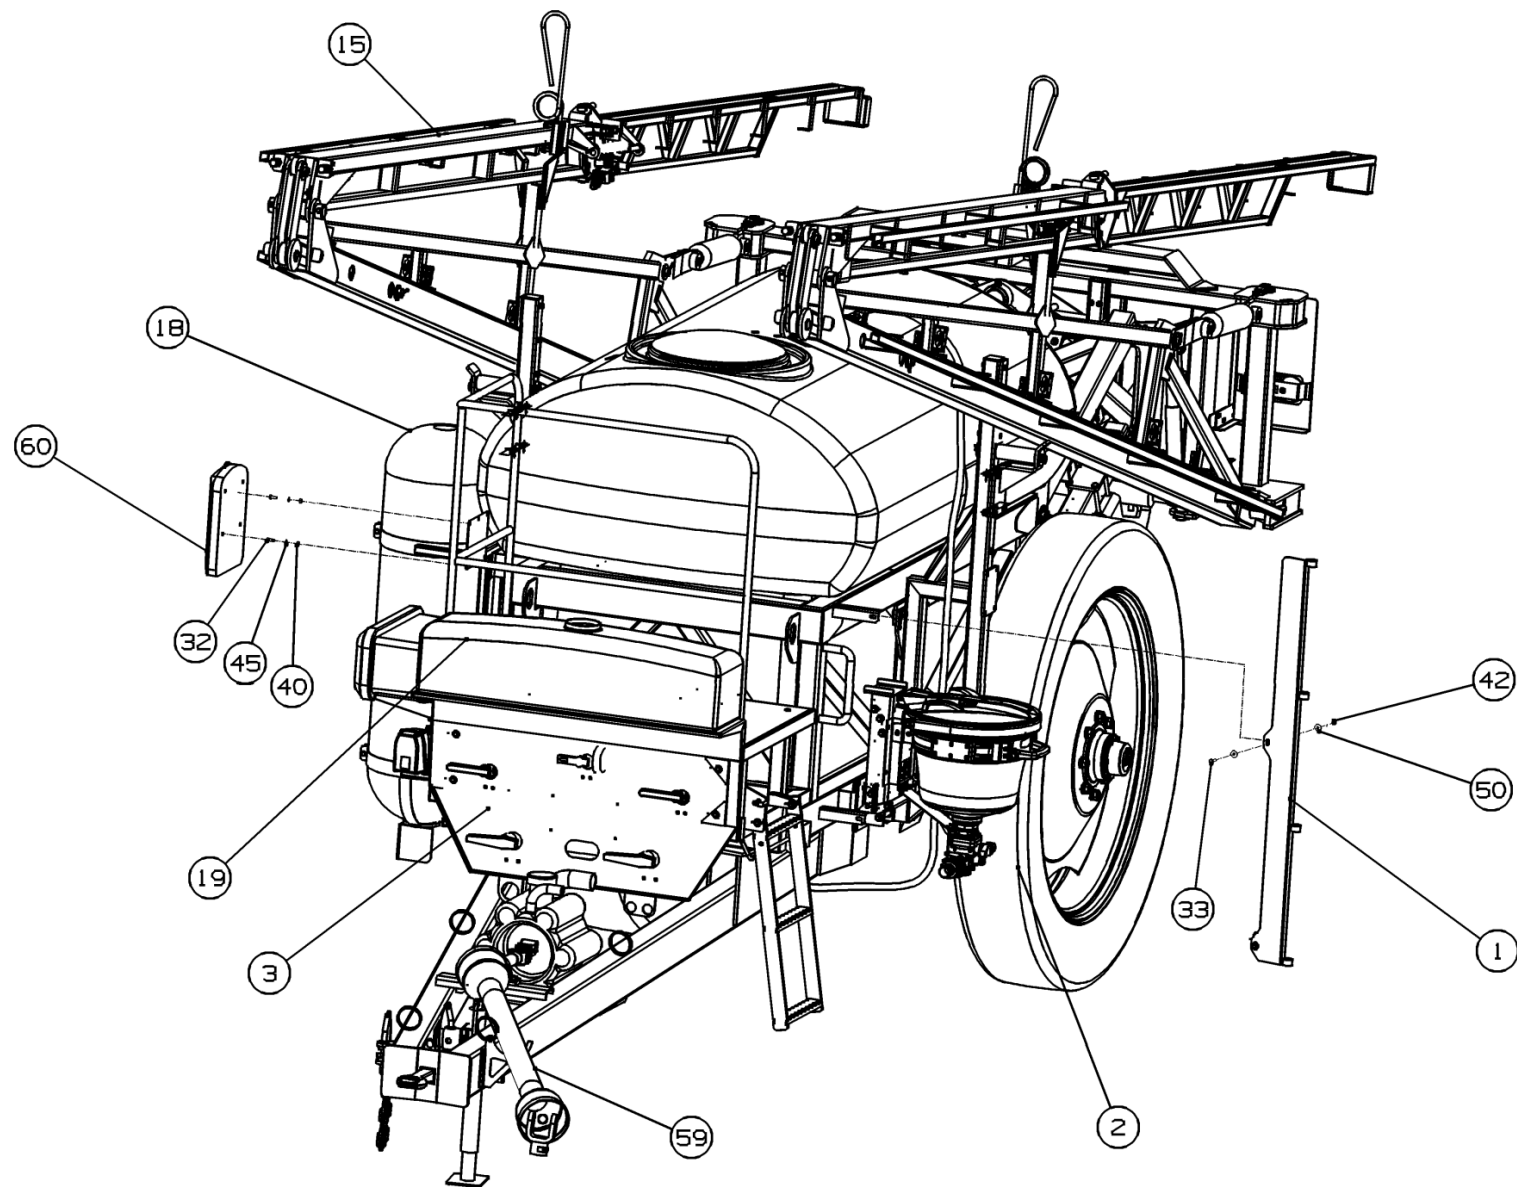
Опрыскиватель полуприцепной ОП-3200-24.01.00.000Б (вид спереди)
